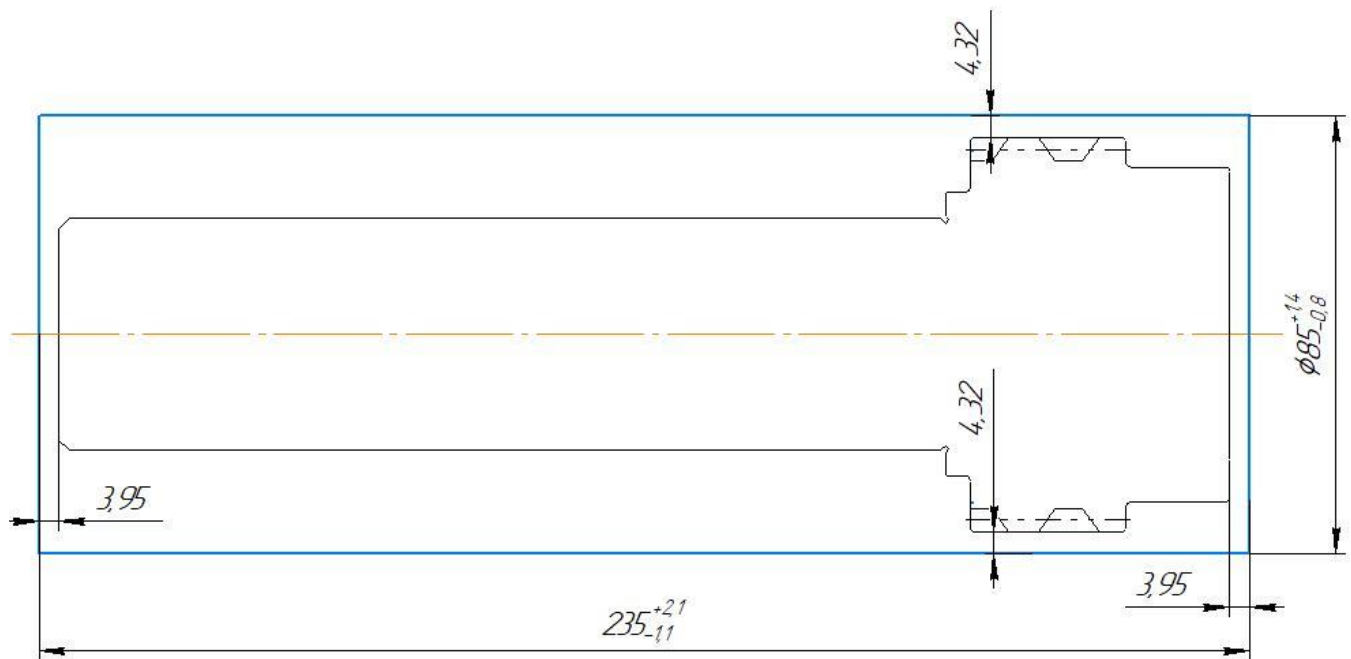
Заготовка, яка виготовлена із круглого прокату
